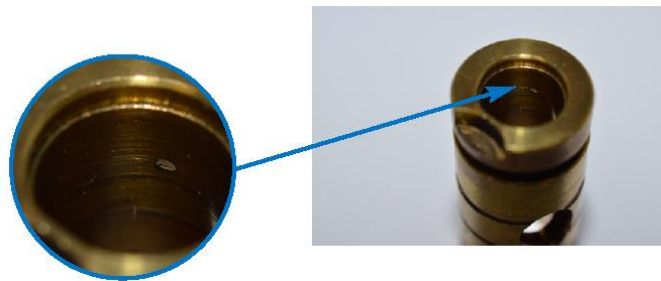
Зношування внутрішньої поверхні підшипника турбокомпресора
